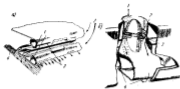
Конструкция вентилятора, раскатываемого по вершине дельта:
